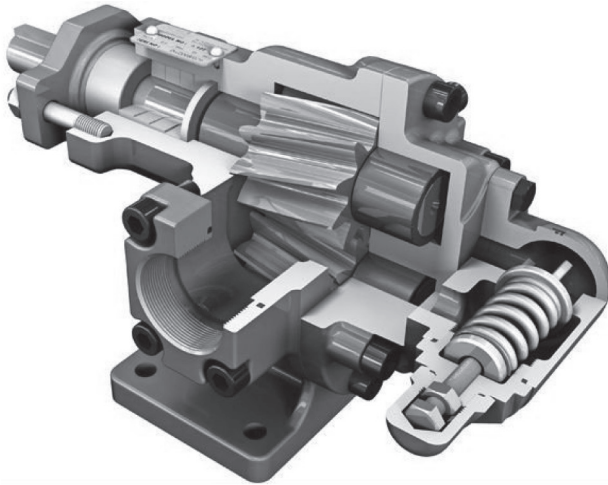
Pormenor construtivo da bomba de engrenagens exteriores (Fonte: Bosch).
